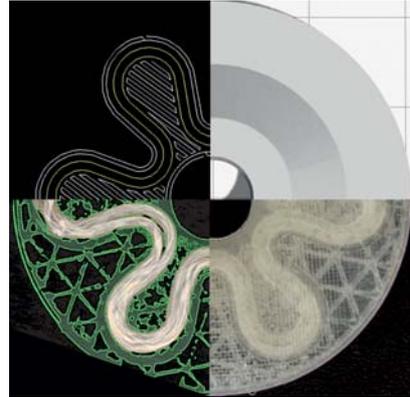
Insert-Prüfteil, von links/oben: CAD-Ansicht, Makrobild, XCT-Schnittbild, Slideansicht der Faserschlaufen
